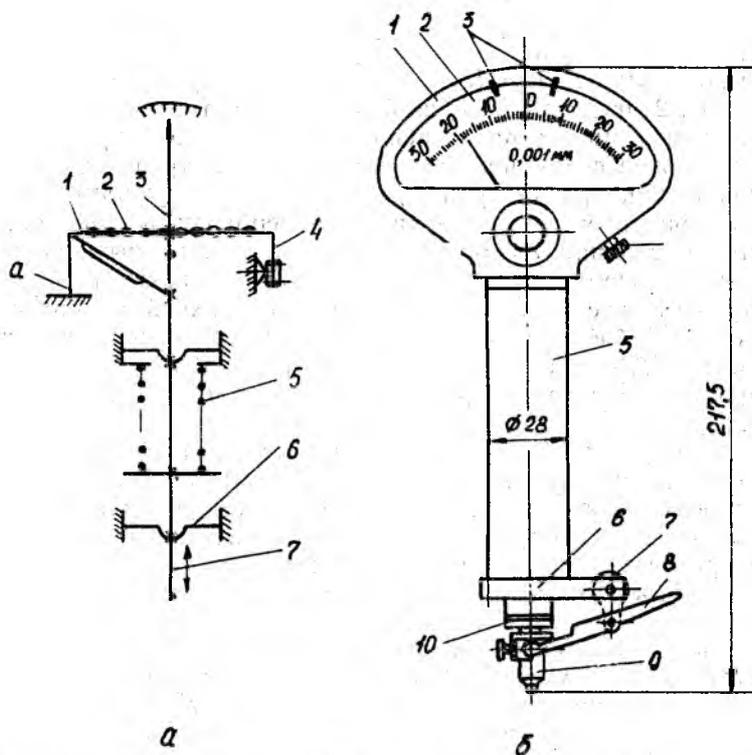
Пружинная измерительная головка ИГП — микрокатор: а — схема; б — внешний вид
